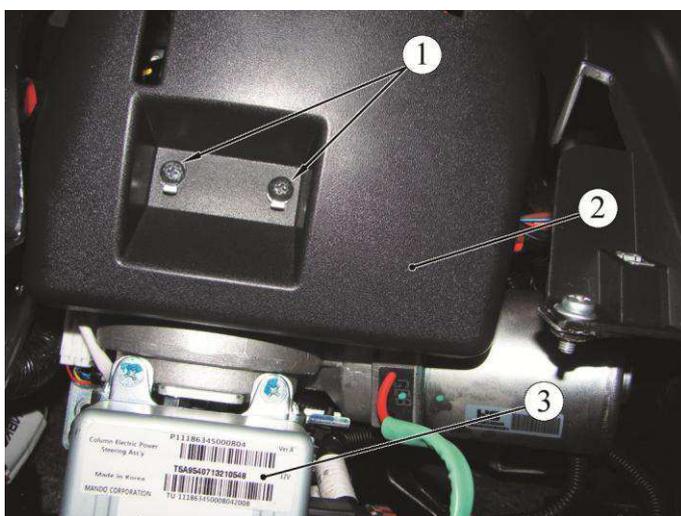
Кожух облицовочный нижний вала рулевого управления:
